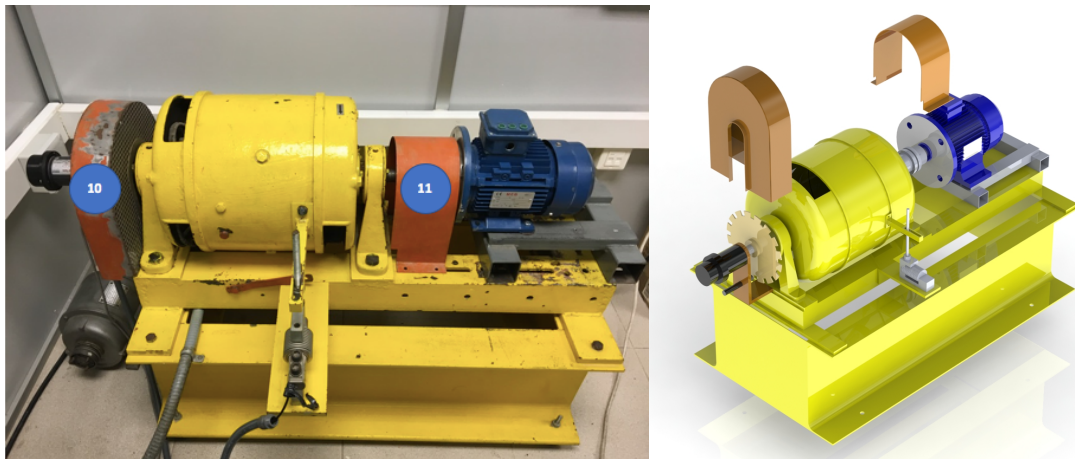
Proteccions i explosionat del banc d'assaig amb SolidWorks
